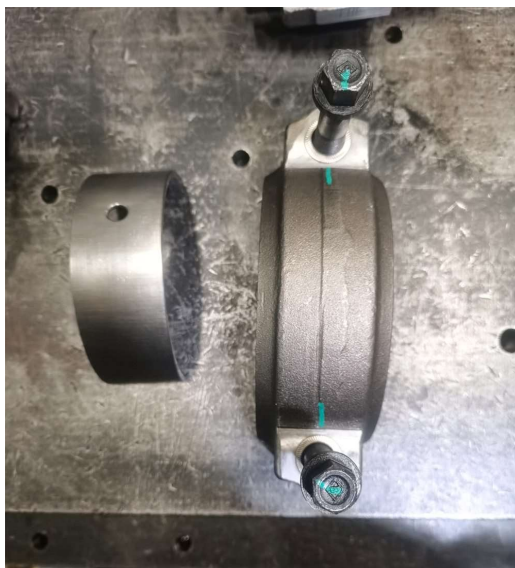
Крышка шатуна, крепёжные болты и вкладыш
